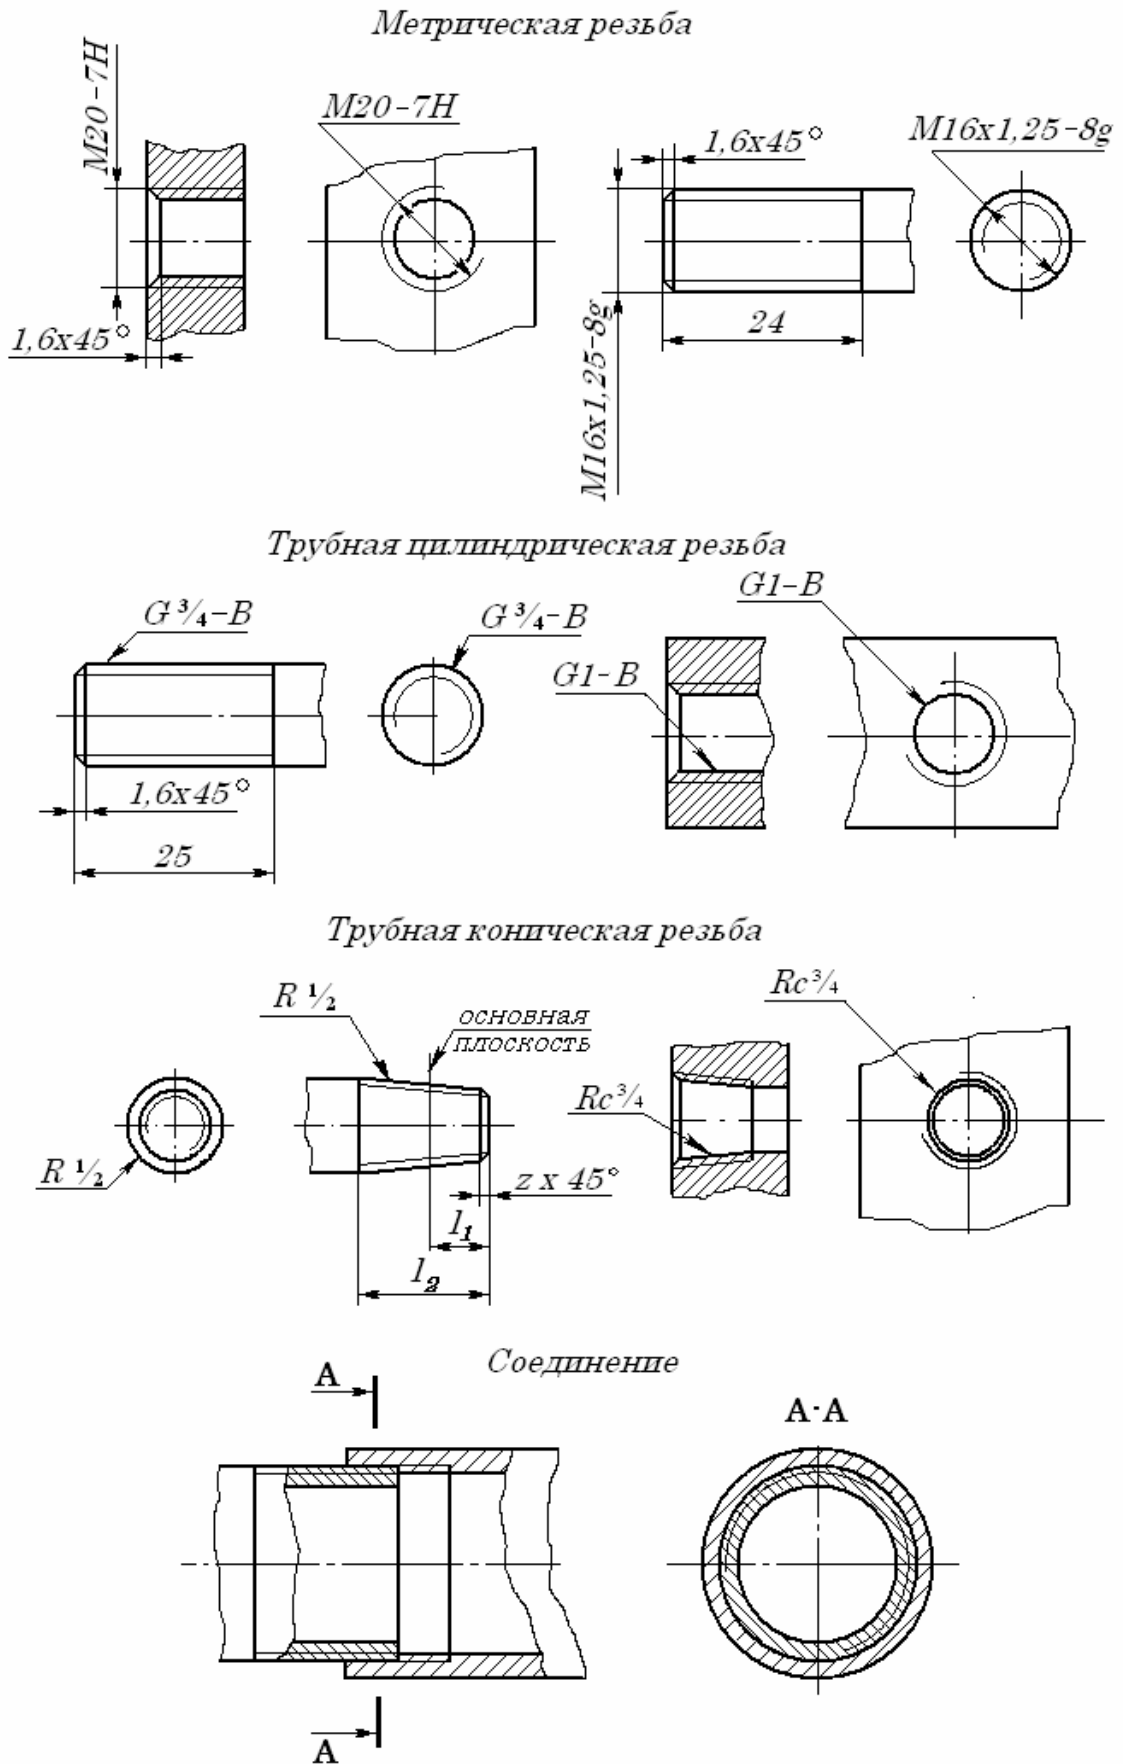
Примеры обозначения резьбы и резьбовых соединений
